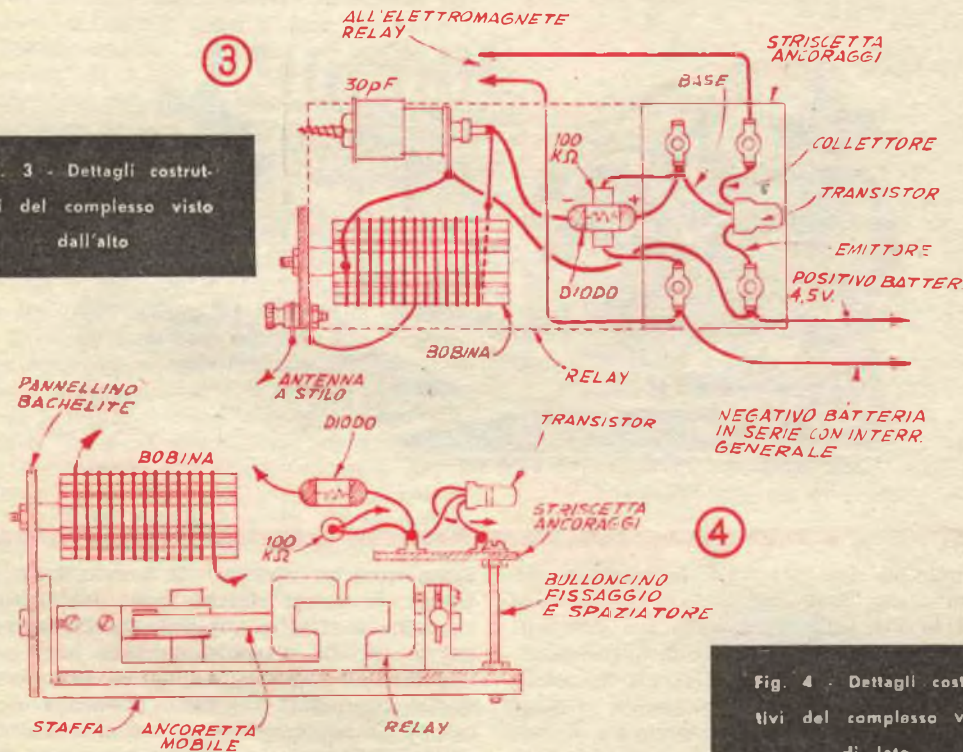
Dettagli costruttivi del complesso visto di lato
